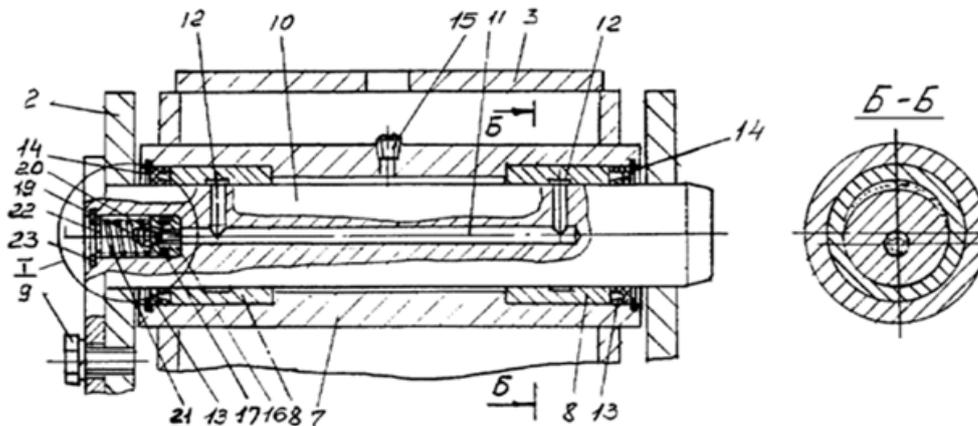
Шарнир манипулятор лесозаготовительной машины
